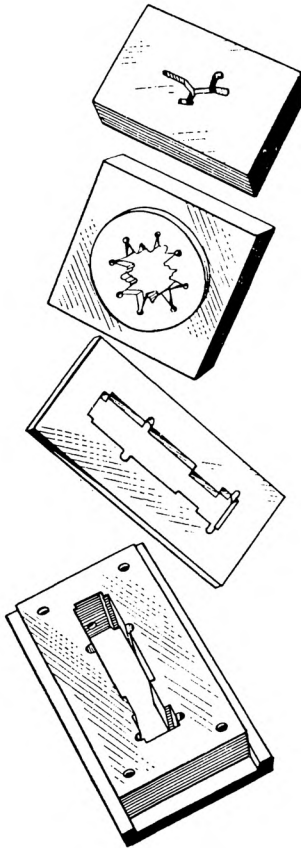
Образцы изделий, обрабатываемых ленточной пилой
